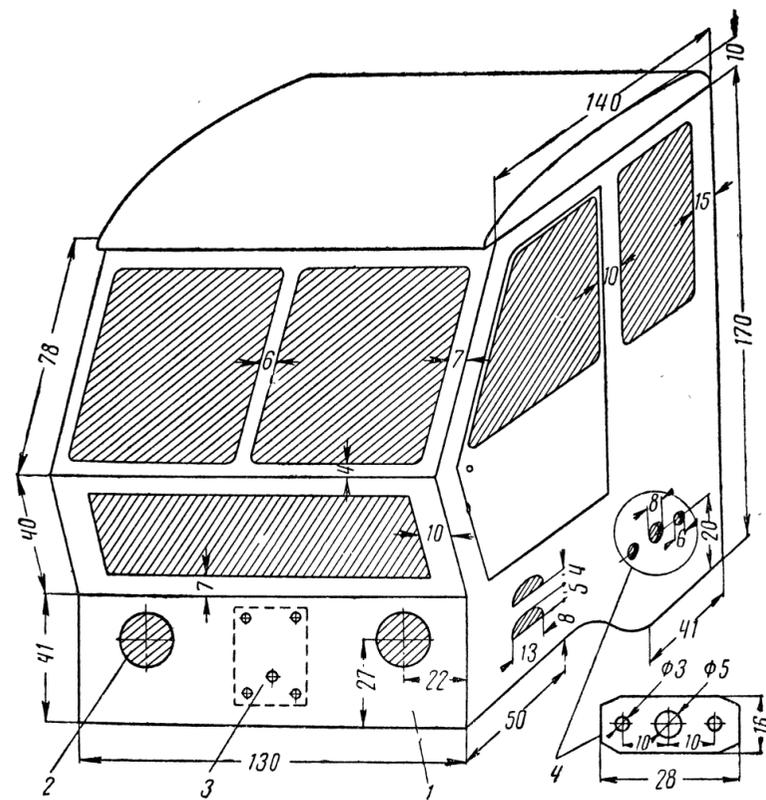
Кабина: 1—передняя стена кабины; 2—отверстие для фары; 3—место крепления швеллерной рамы; 4—подшипник задней оси
